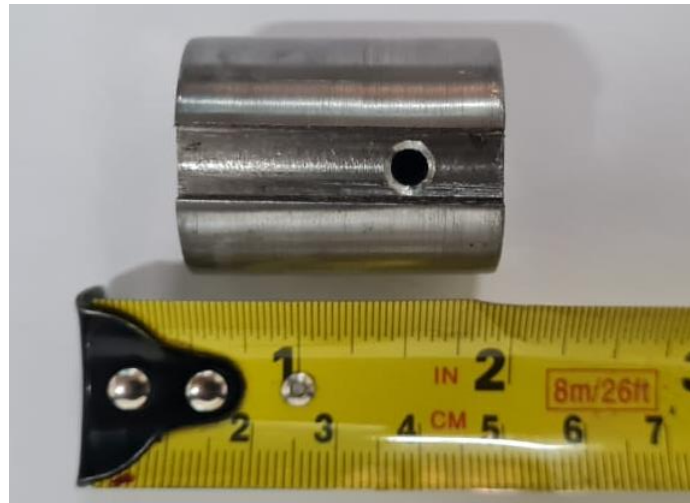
Bucha com parte do tarugo não-usinado, antes do processo de corte.
